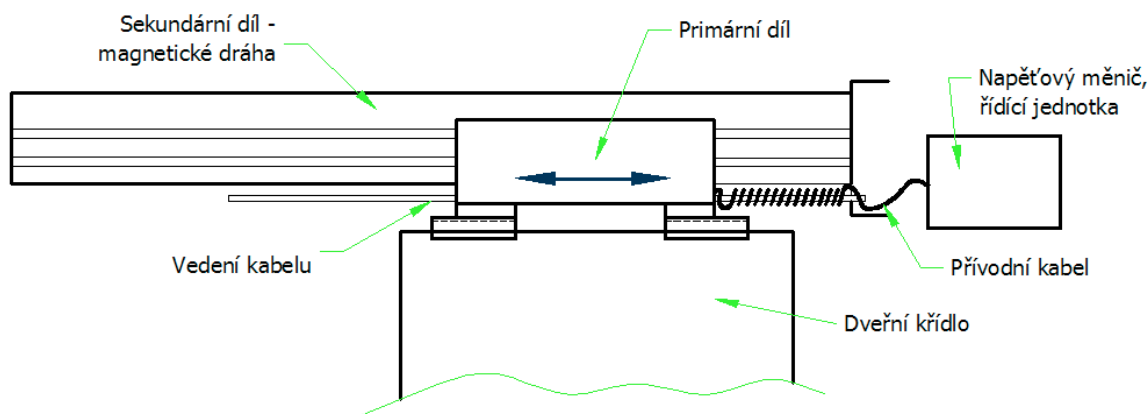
Fyzikální princip lineárního elektromotoru [9]
